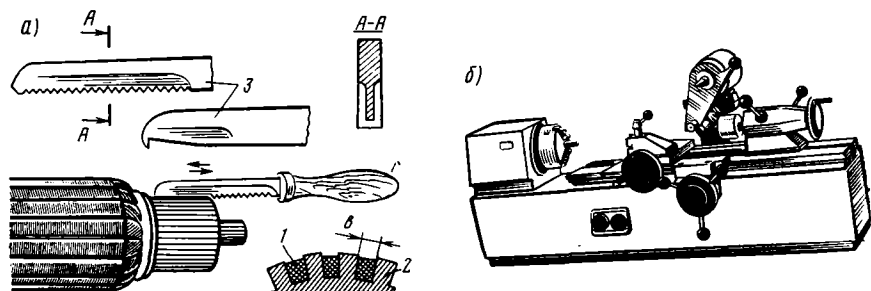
Углубление миканитовой изоляции между пластинами якоря и обточка коллектора якоря генератора:
